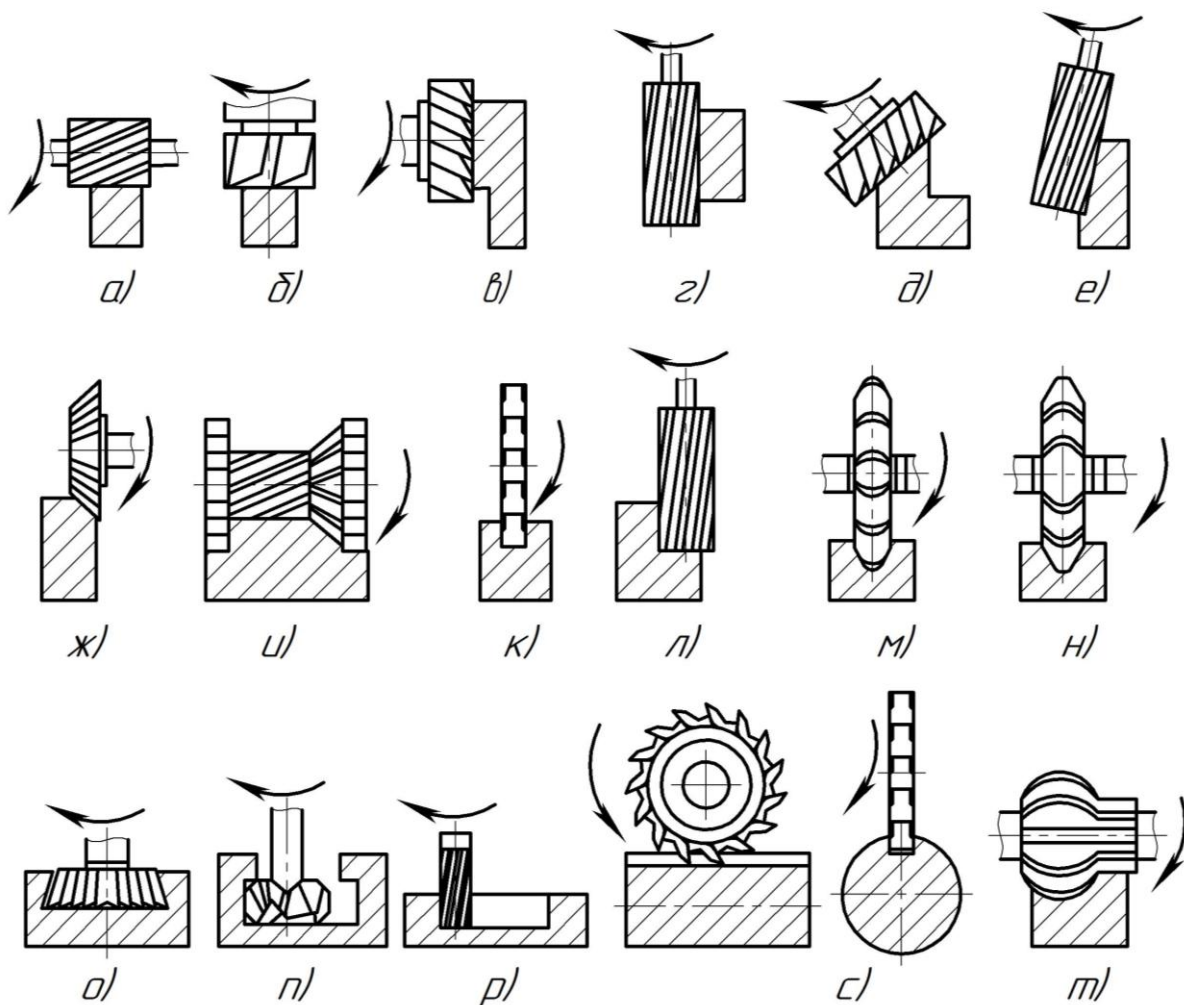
Схеми обробки поверхонь на фрезерних верстатах
